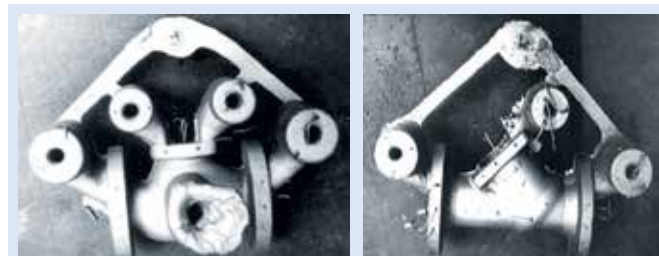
Отлитые корпуса клапана из стали 10X18H9ТЛ, $D_y = 6,5 \text{ см}$
